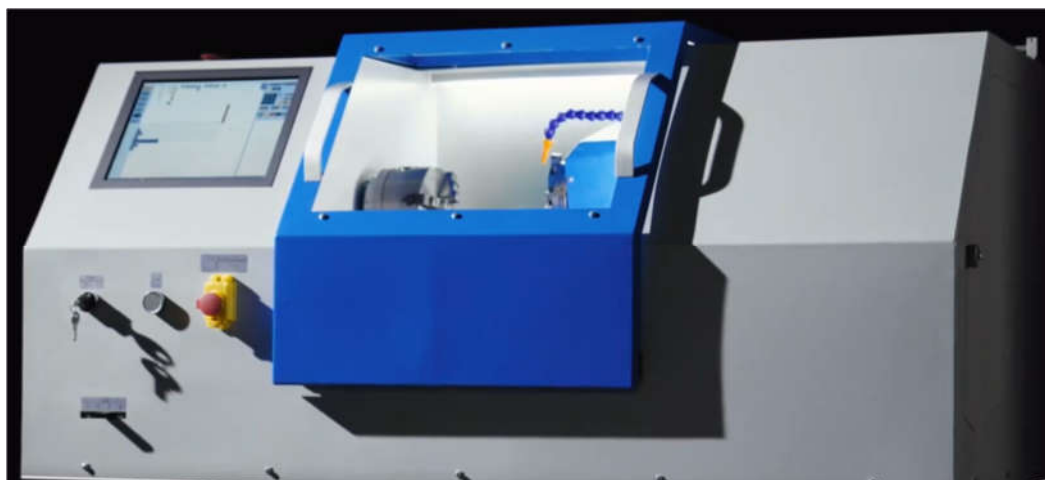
Внешний вид станка с ЧПУ модели УТС6
